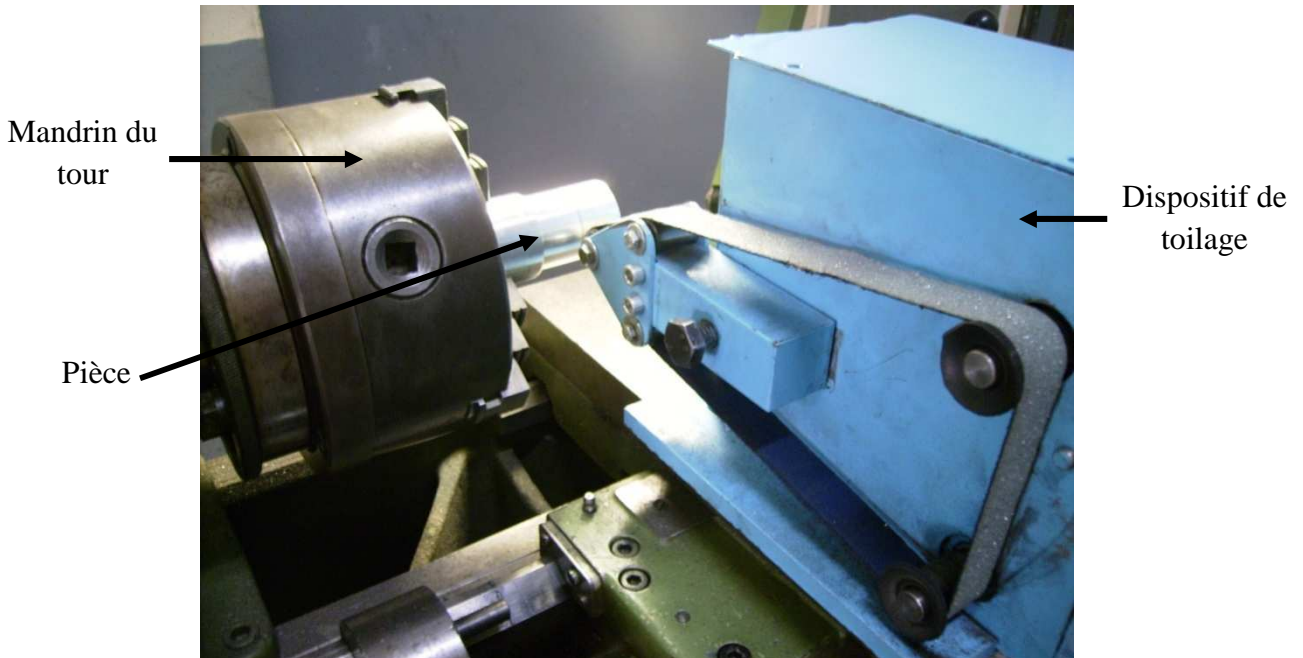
Montage de dispositif sur le Tour Vue à gauche.
